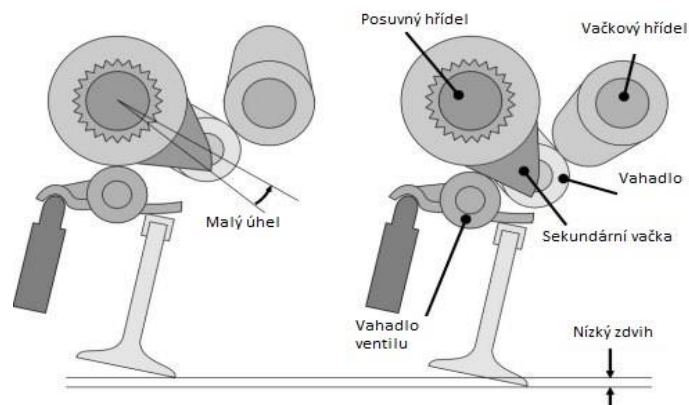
Schéma funkce systému BMW Valvetronic [33]
